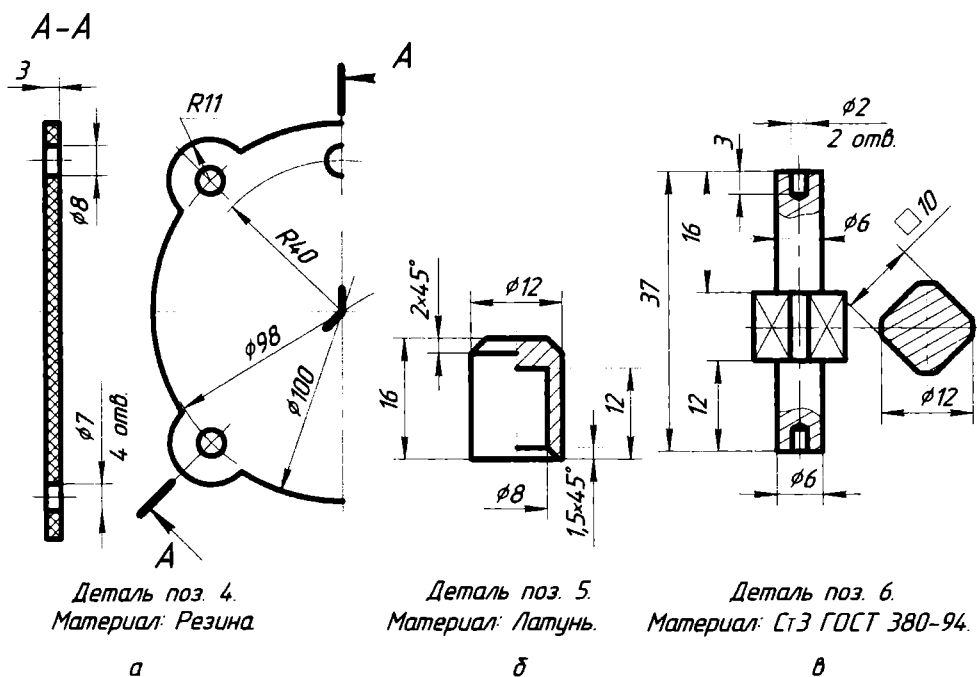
Чертежи: а — диафрагмы; б — плунжера; в — толкателя
